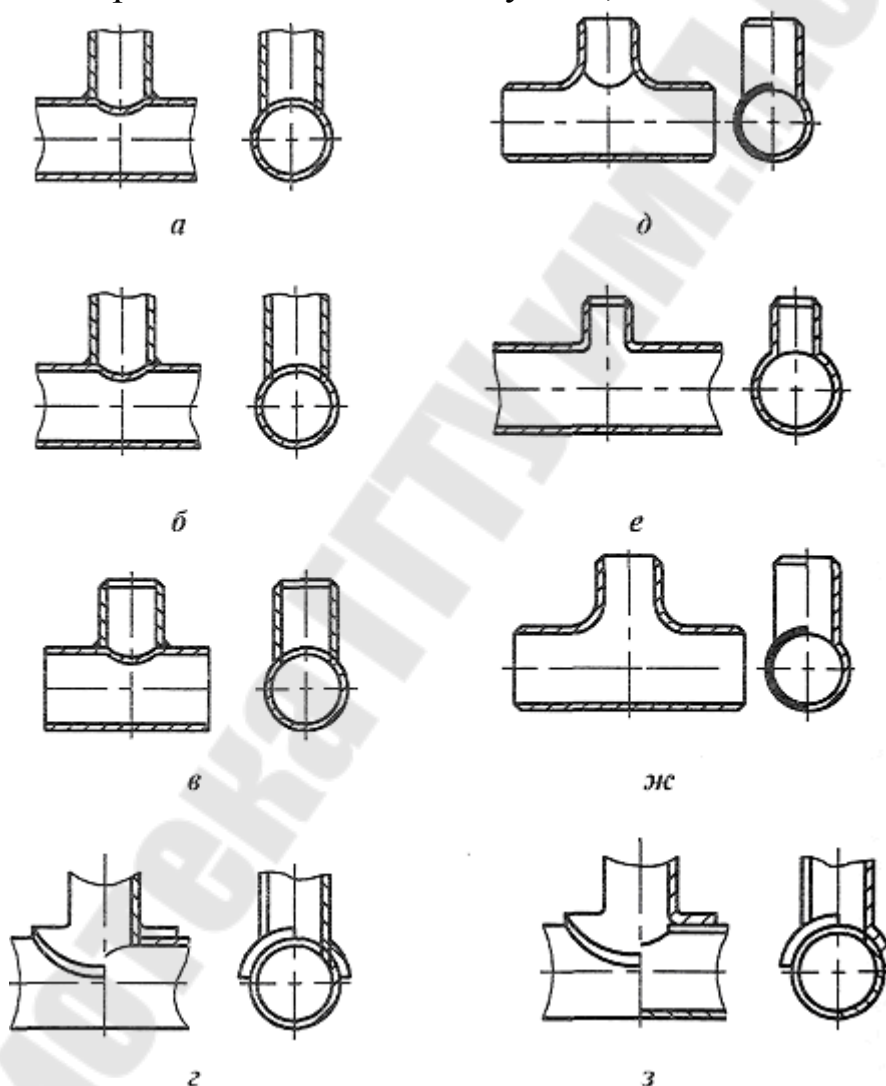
Ответвления и тройники: а - врезка без укрепляющих элементов; б - врезка с усиленным штуцером; в - врезка с усиленным корпусом (сварной тройник); г - врезка с накладным воротником; д - штампованный тройник; е - отбортованный в трубе штуцер; ж - врезная седловина; з - накладная седловина
